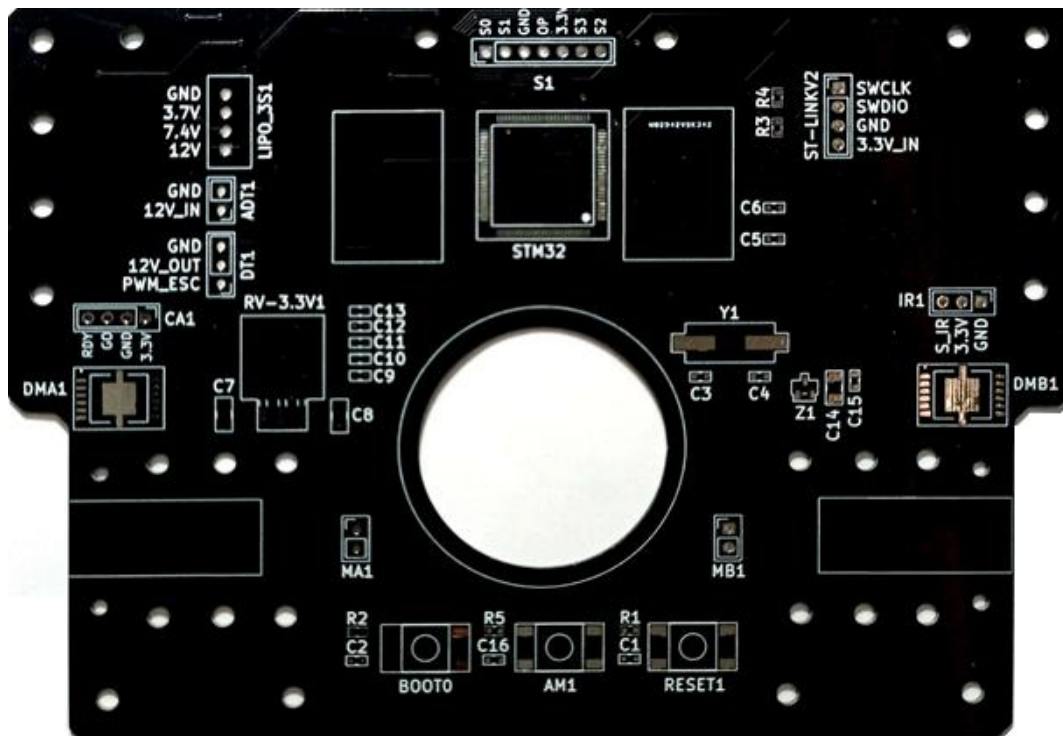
Vista Frontal de la PCB Fabricada del Robot Seguidor de Línea.
